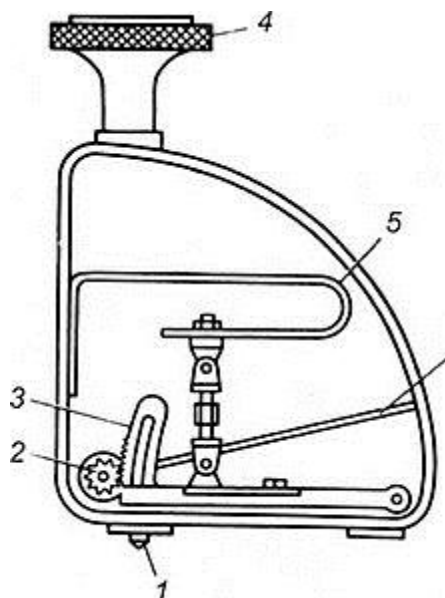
Твердомер Шора: 7 — игла; 2 — зубчатые колеса; 3 — зубчатый сектор; 4 — головка; 5 — пружина; 6 — стрелка прибора
